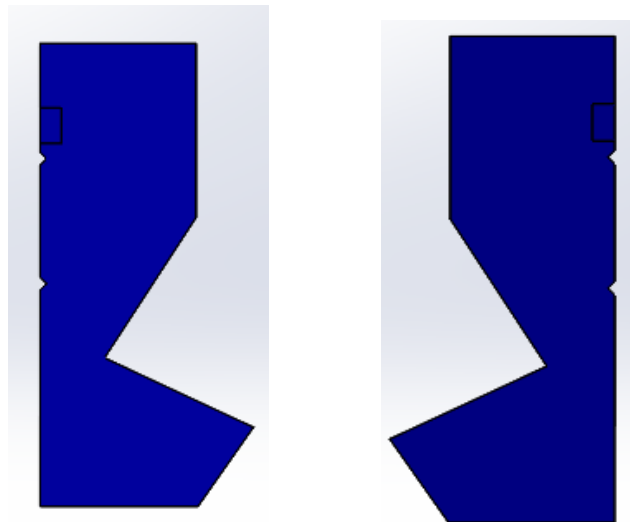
, Piezas Laterales 2) Pieza "Derecha", b) Pieza "Izquierda"
